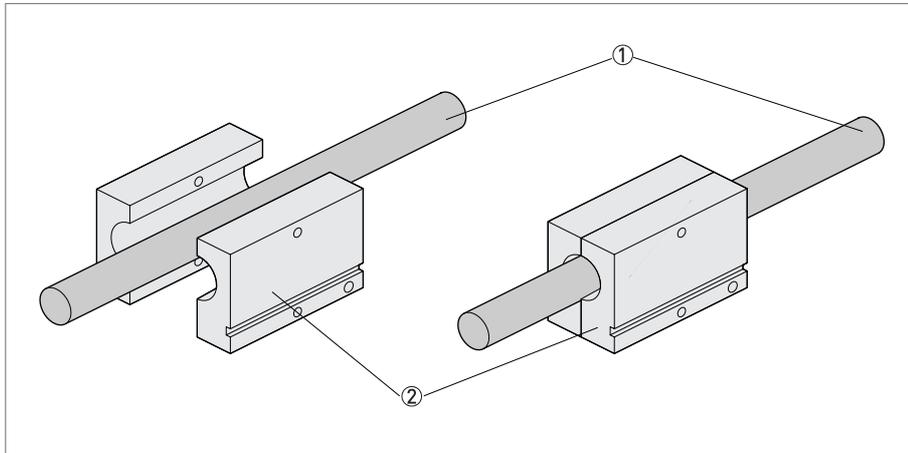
Colocación del soporte de la barra alrededor de la barra
